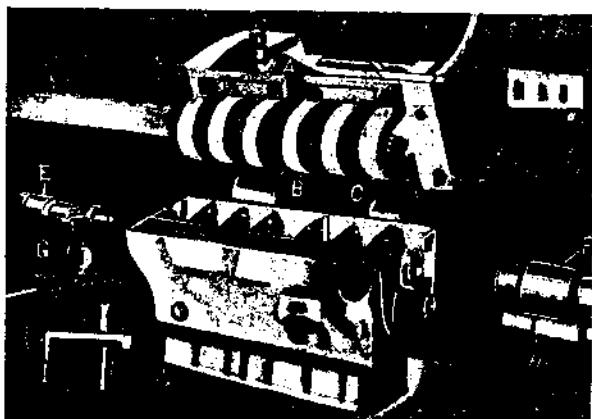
Приспособление Graham-Paige для быстрой установки борштанги.
